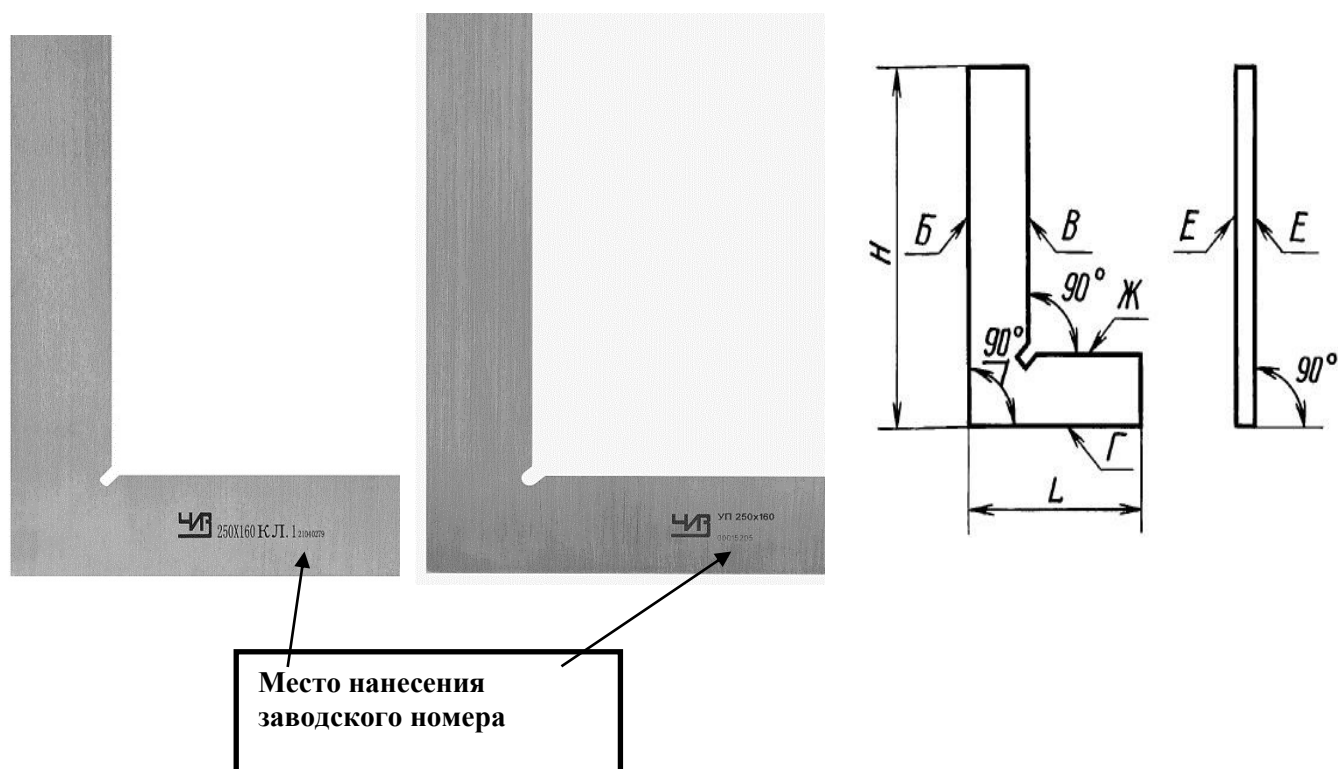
Общий вид угольников типа УП с местом нанесения заводского номера и обозначение условных размеров и поверхностей
